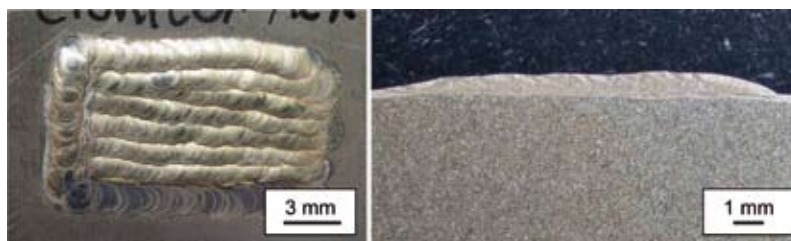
Manuell ausgeführte Auftragschweißung mit dem Zusatzwerkstoff 12-A-Multi (links) und Querschliff (rechts)
